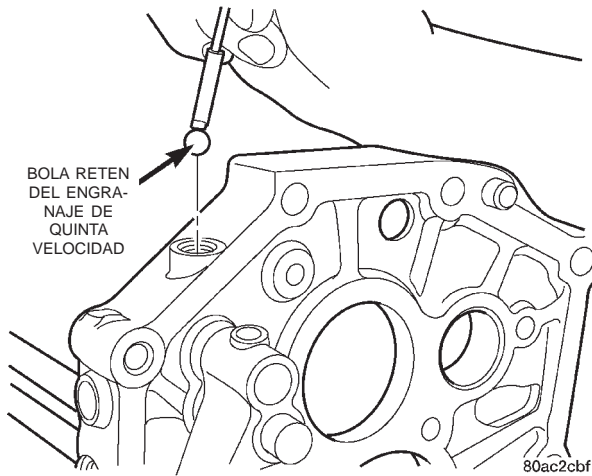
Desmontaje de la bola retén del engranaje de quinta velocidad
